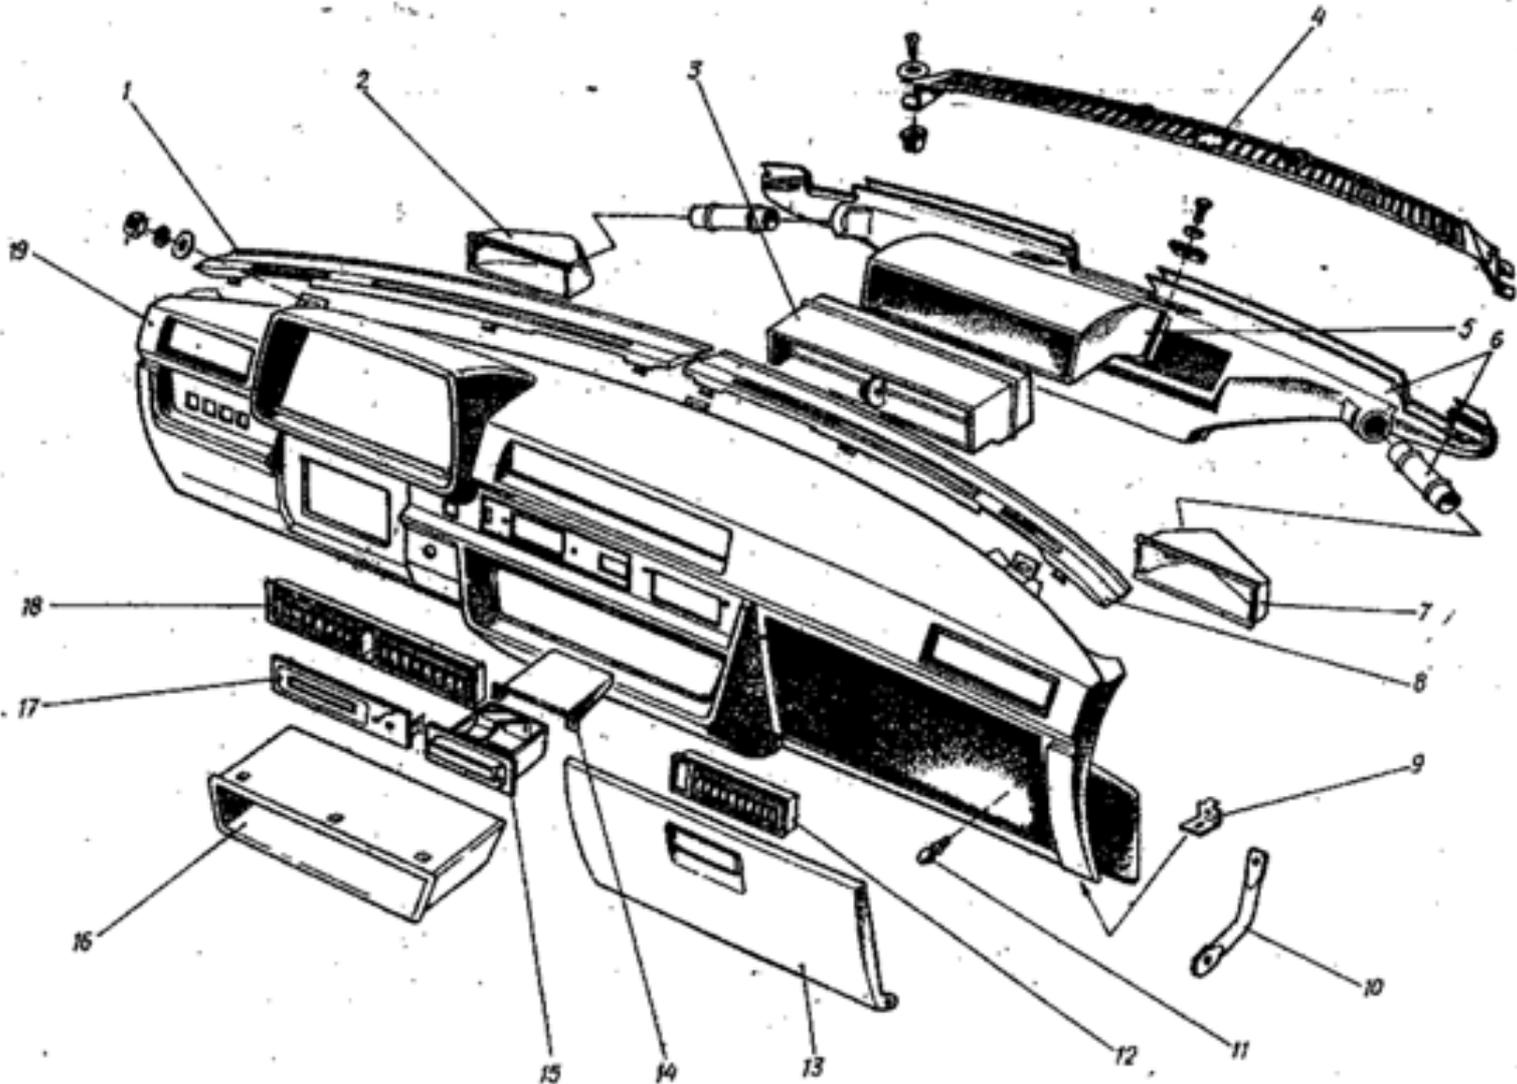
Детали панели приборов 1102-5325016: 1 - накладка левая; 2 - корпус боковой левой; 3 - корпус центральный; 4 - облицовка панели; 5 - наставка; 6 - сопло обдува с патрубками; 7 - корпус боковой правой; 8 - накладка правая; 9 - кронштейн; 10 - кронштейн; 11 - буфер; 12 - рамка боковая; 13 - дверца ящика; 14 - гнездо пепельницы; 15 - пепельница; 16 - ящик перчаточный; 17 - вставка; 18 - рамка центральная; 19 - панель приборов.
